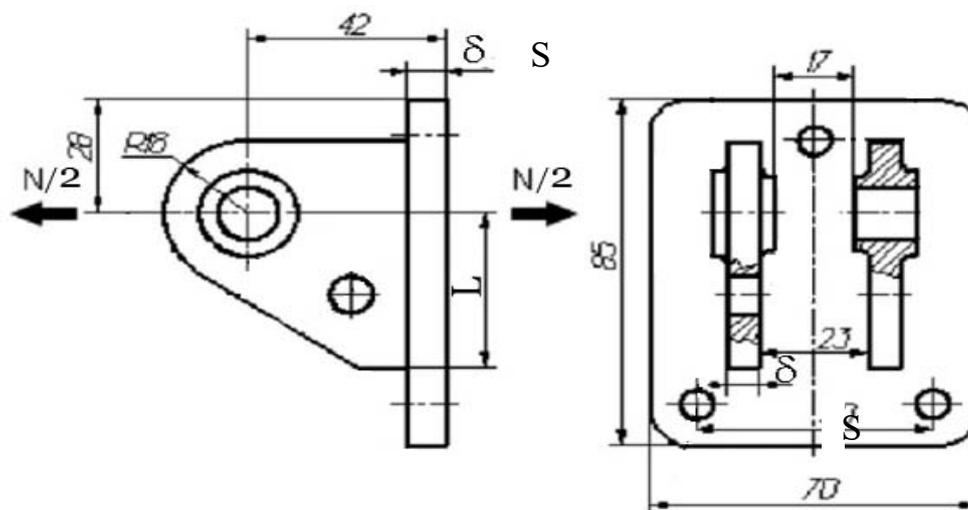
Расчетная схема сварного соединения
